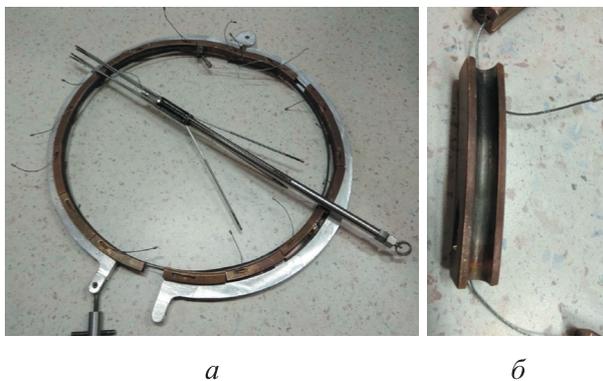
Внешний вид защитного приспособления после извлечения из баллона (а) и сектора приспособления после сварки (б)
